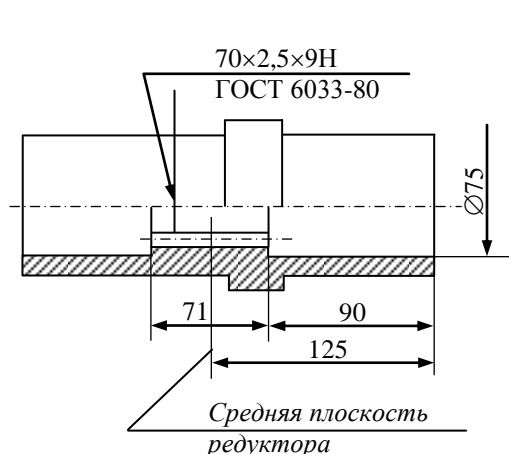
П7 Присоединительные размеры вала редуктора 1Ц2У-200
